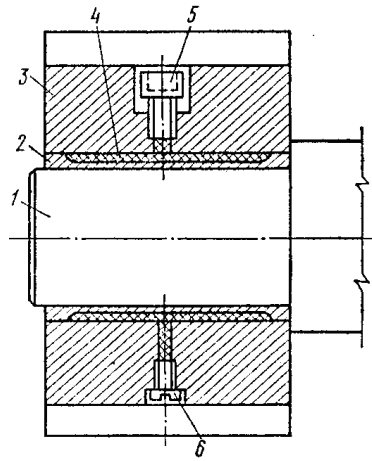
Схема гідропластмасового закріплення фрези на шпинделі: 1 — шпиндель, 2 — втулка тонкостінна, 3 — фреза, 4 — гідропластмаса, 5 — гвинт-плунжер, 6 — гвинт
